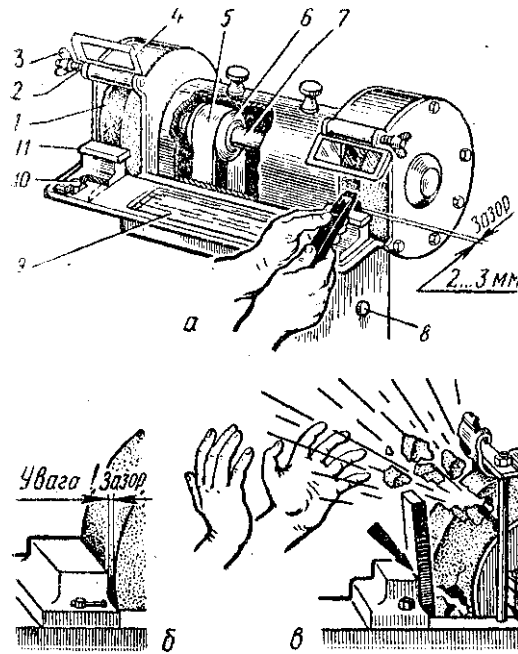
Загострювання зубила на загострювальному верстаті (а) та встановлення підручника (б, в):
